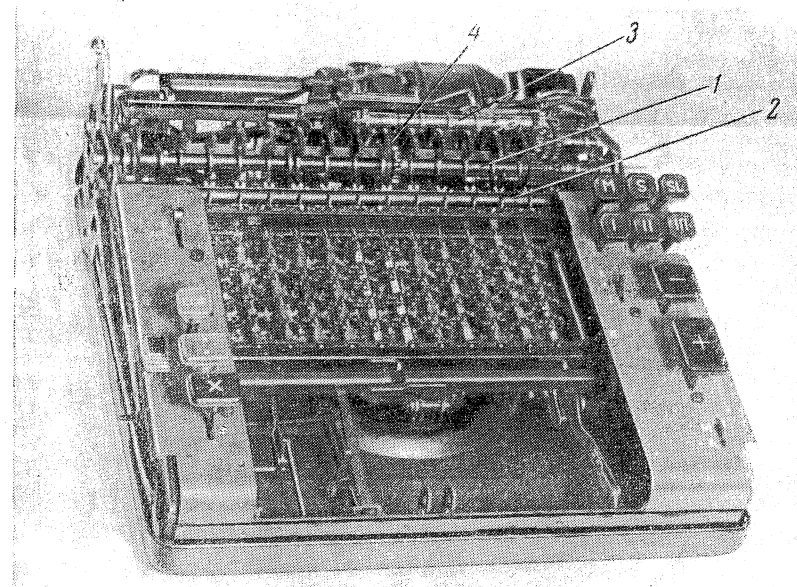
Основной и промежуточный валы и вал счётчика оборотов. 1—основной вал, 2—промежуточный вал, 3—вал счётчика оборотов, 4—секторы основного вала.
